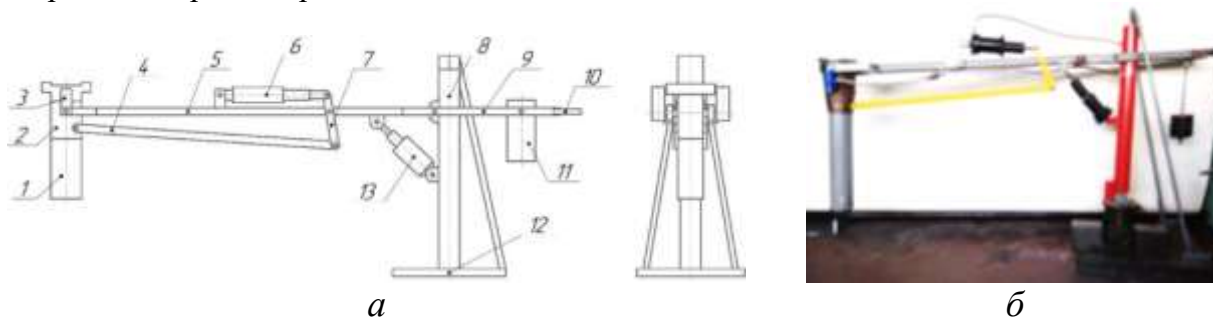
Конструктивная схема (а) и опытный образец (б)
